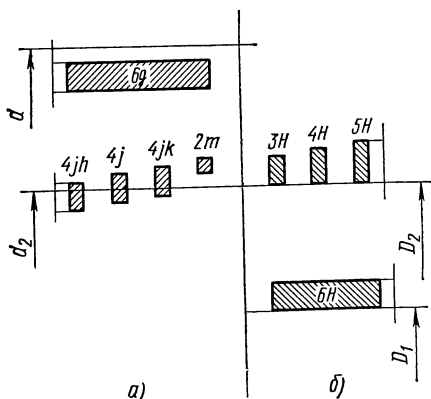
Расположения полей допусков для образования переходных посадок: а — для наружной резьбы, б — для внутренней резьбы
